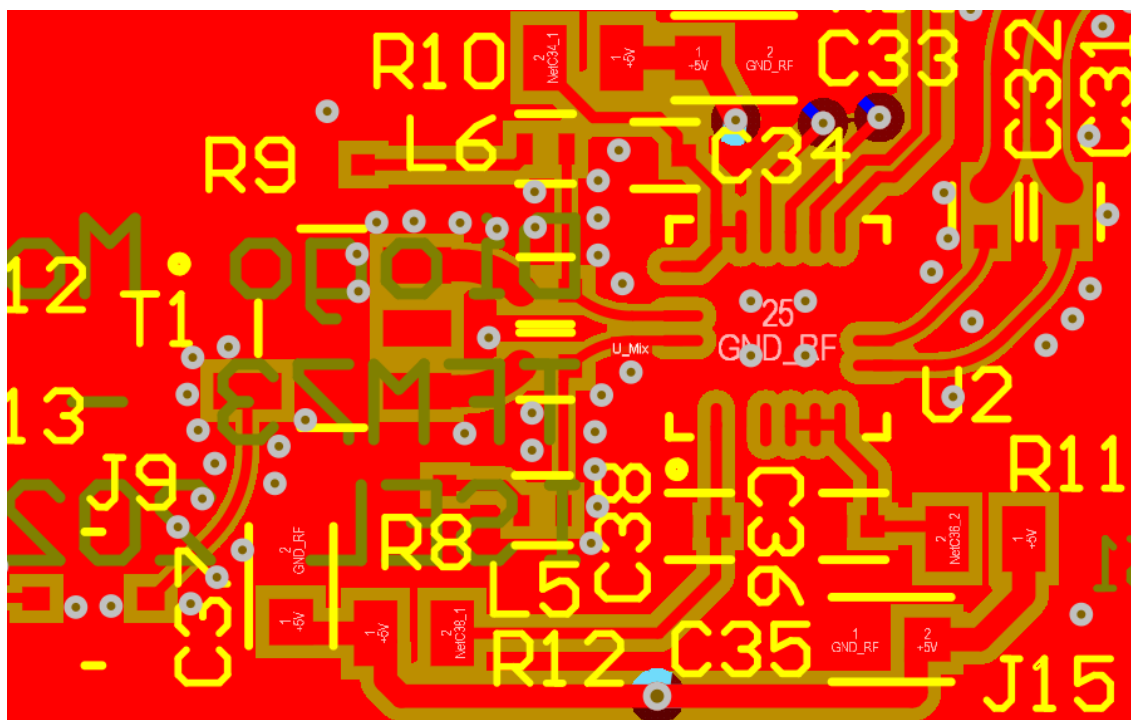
Desenho do layout da PCB do desmodulador I/Q
